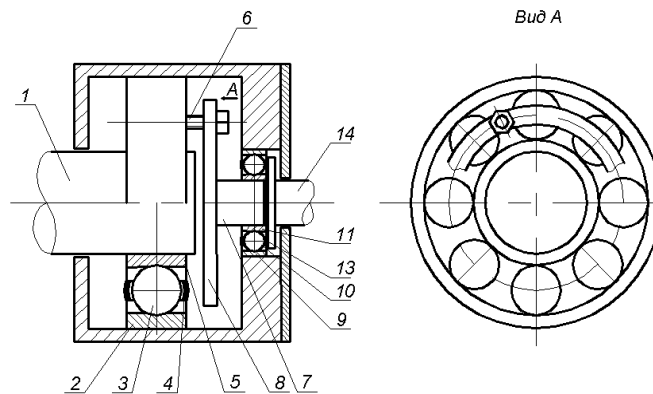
Схема двухступенчатого подшипник – планетарного редуктора:
